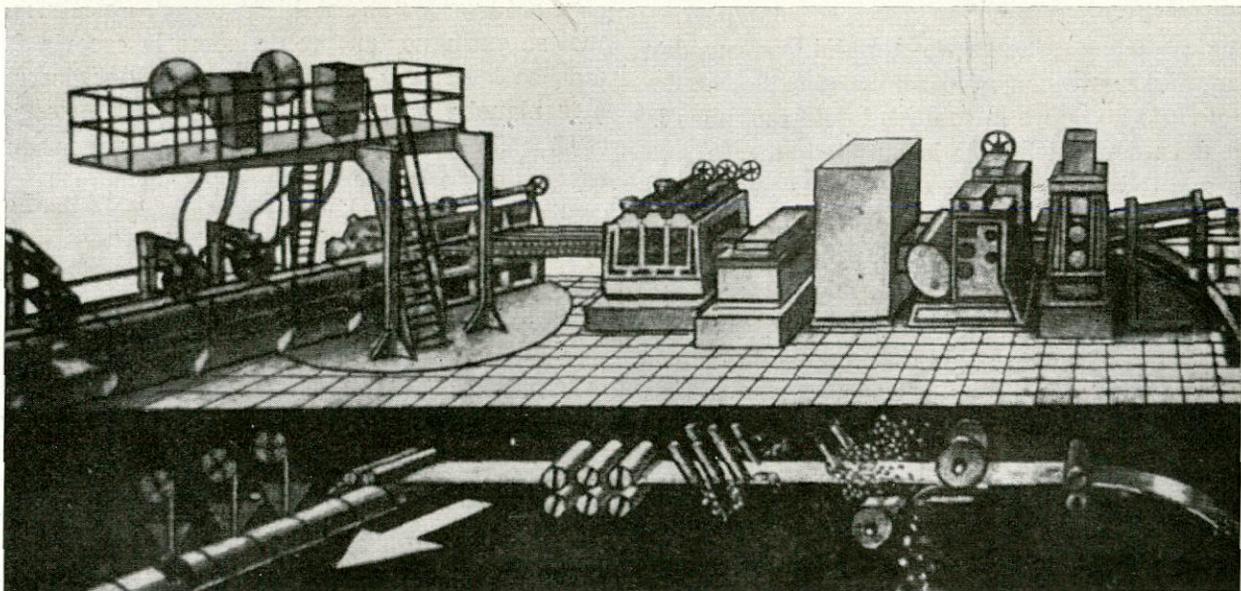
Instalación automática para la soldadura en espiral de tubos.
